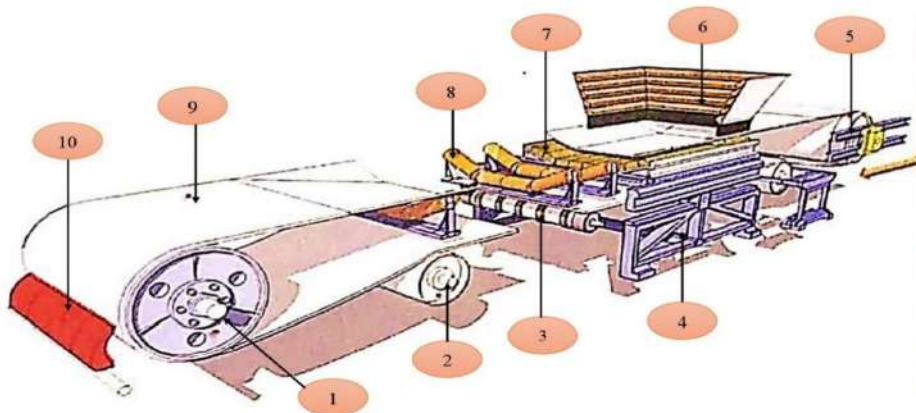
Ленточный конвейер: 1 – приводной барабан; 2 – отклоняющий барабан; 3 – ролик-опора нижней ветви; 4 – опорная конструкция; 5 – концевой барабан (натяжная станция); 6 – загрузочное устройство; 7 – демпферная станция; 8 – ролик-опора верхней ветви; 9 – конвейерная лента; 10 – очистное устройство
